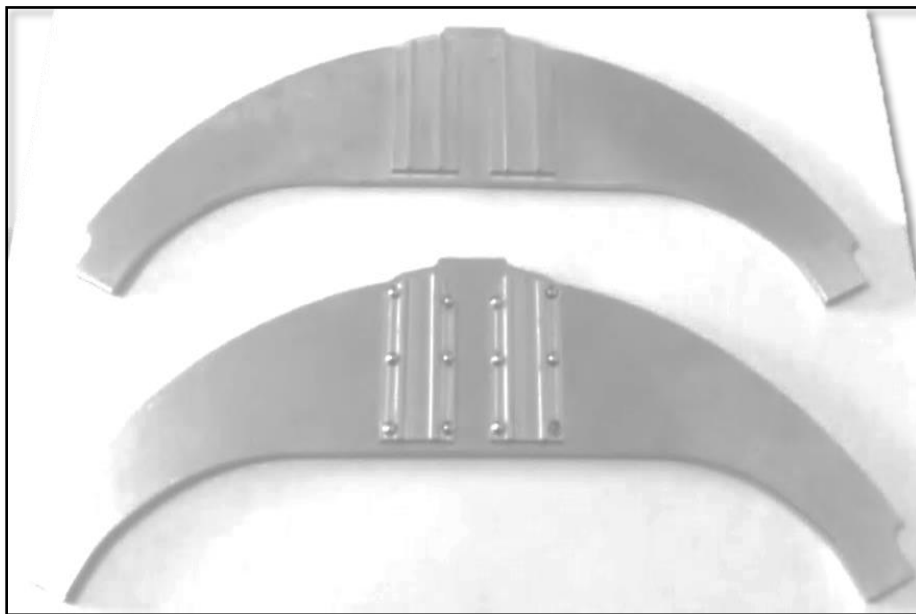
Pieza ensamblada por remaches y unitaria de aluminio 6061 T6.
